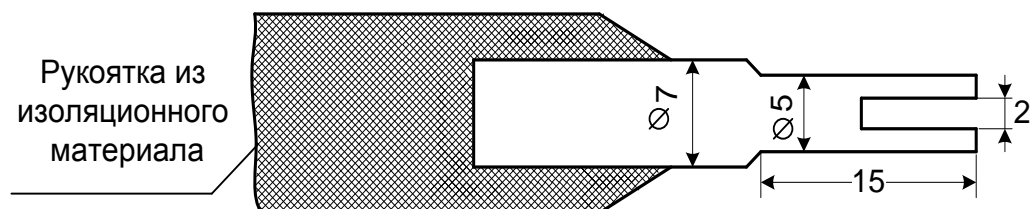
Приспособление для регулировки пружин автопереключателя
